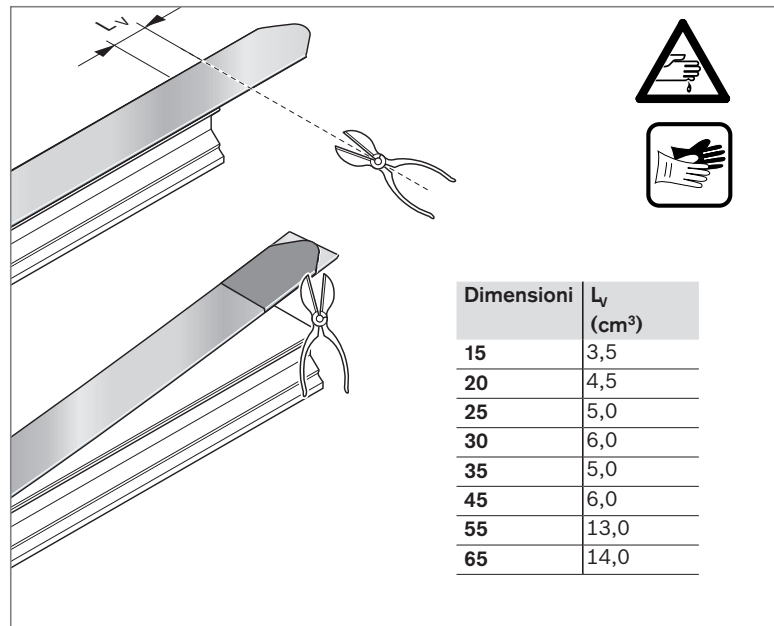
Montaggio dei nastri di protezione più lunghi della rotaia
